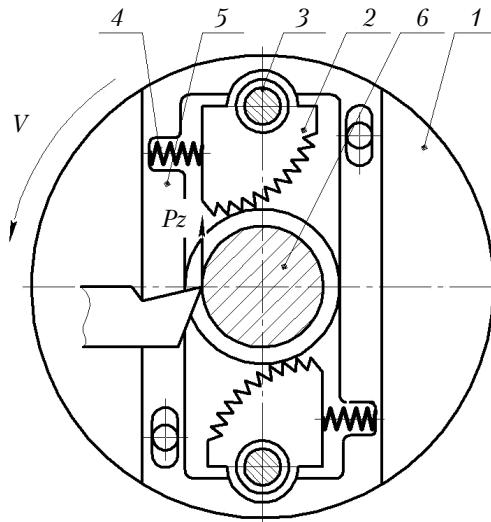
схема токарного поводкового патрона с приводом от сил резания
